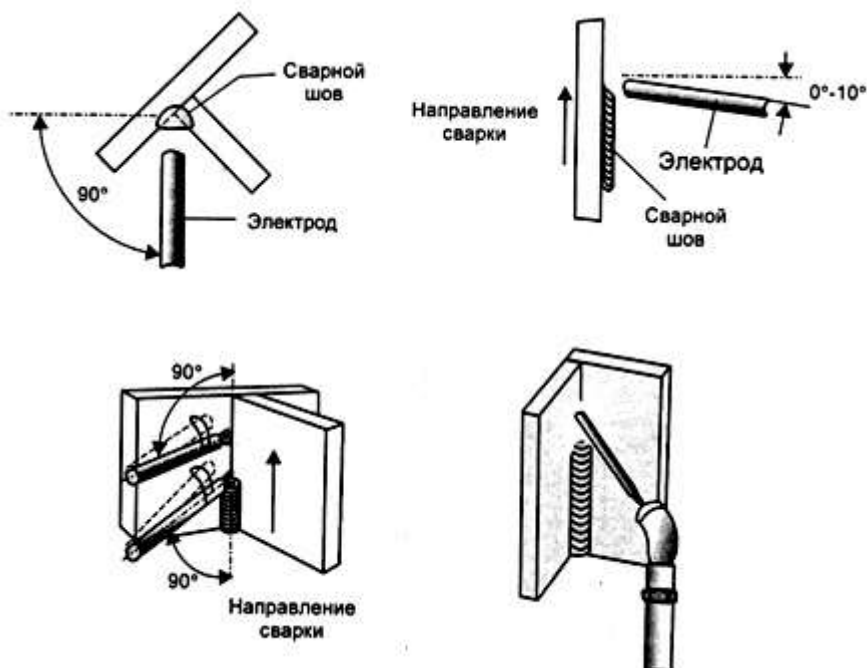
Положение электрода при сварке таврового соединения в вертикальном положении однопроходным угловым швом.
